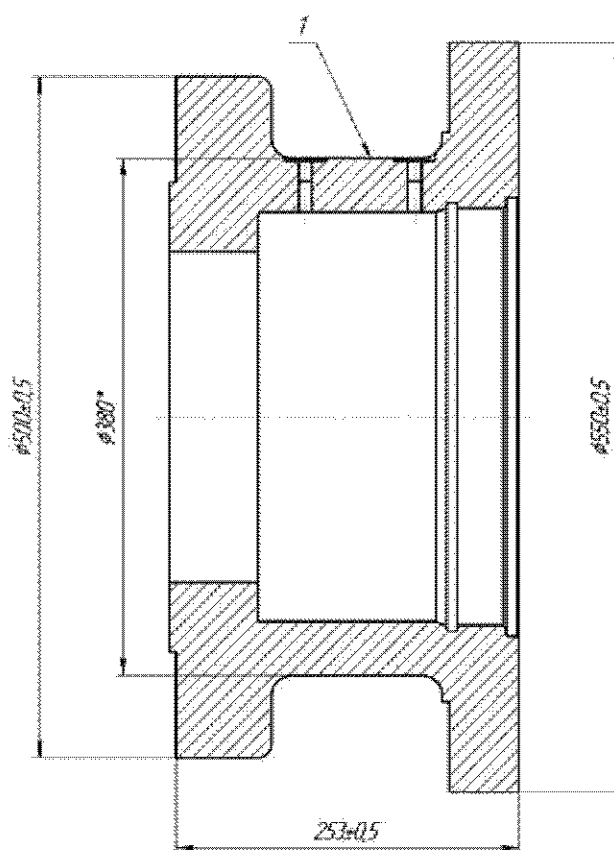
Корпус с поверхностью для захвата промышленным роботом
